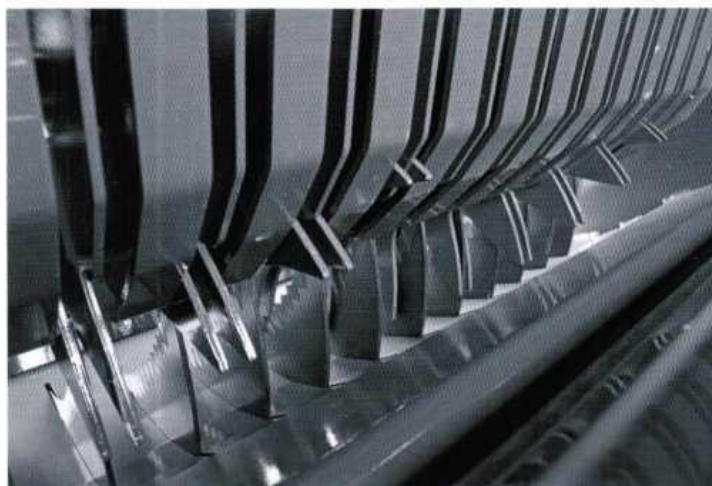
Вид режущей системы ROTO GUT с 14 ножами
